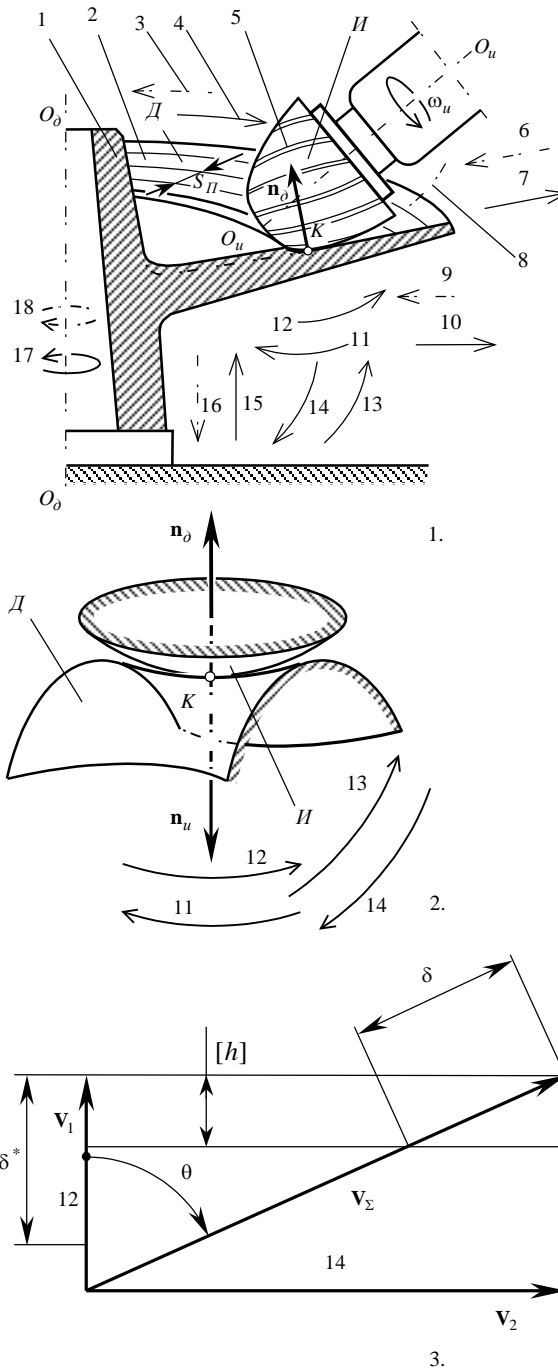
Схема способа обработки сложных поверхностей деталей (а.с. №1336366).
